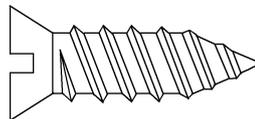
Gewindeformende Schraube (siehe 3.18)
